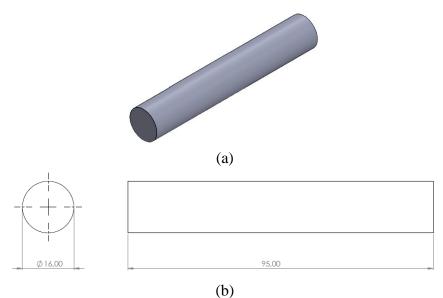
10 (a) Bolt (b) Dimension Bolt
